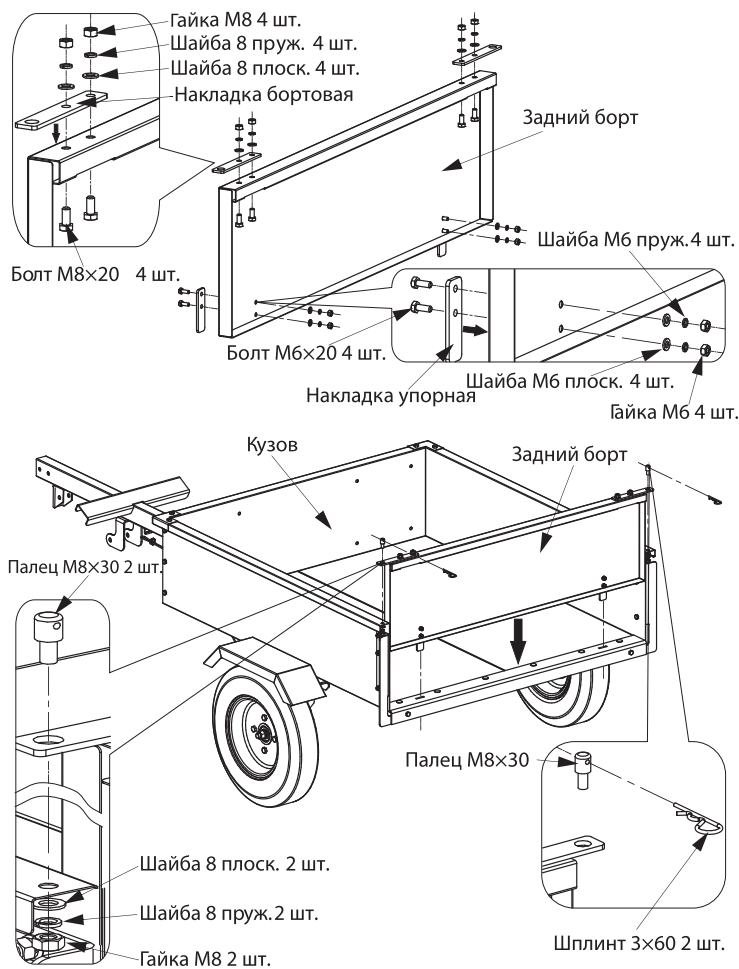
Схема сборки заднего борта и крепление его с кузовом.
